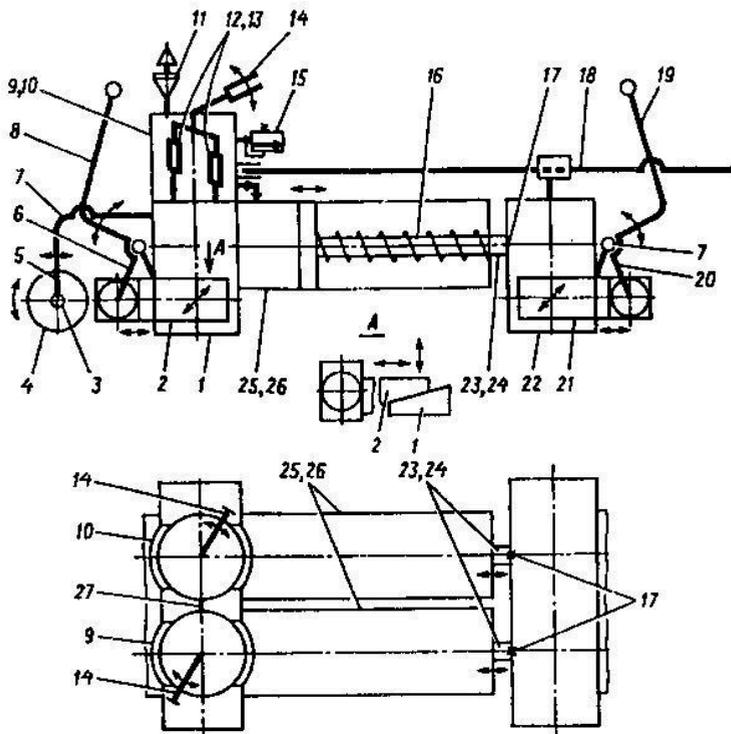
Структурная схема разгонщика Р-25: 1, 22 – корпуса разгонщика; 2, 21 – клинья; 3 – палец; 4 – ролик; 5 – скоба; 6, 20 – поводки; 7 – ось; 8, 19 – рукоятки; 9, 10 – масляные бачки; 11 – заливная пробка; 12, 13 – плунжерные пары; 14 – ручка на конце шлицевого вала; 15 – предохранительный клапан; 16 – стяжная пружина; 17 – шпилька; 18 – съемная рукоятка привода насосов; 23 – шток; 24 – крышка; 25 – крышка цилиндра; 26 – корпус цилиндра; 27 – полиэтиленовая трубка
